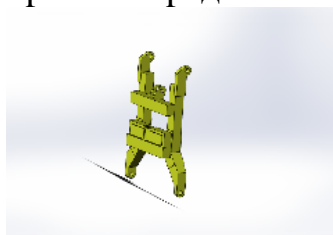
Общий вид разрабатываемого рычага противовеса
